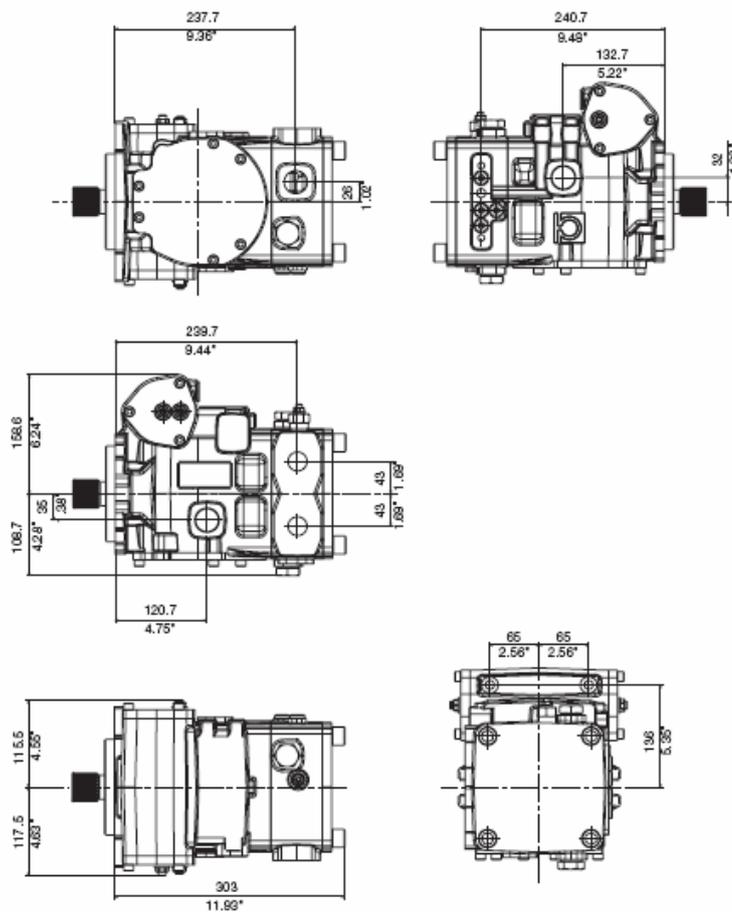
Габаритные и присоединительные размеры насосов НР Р7 и НР Р8..
